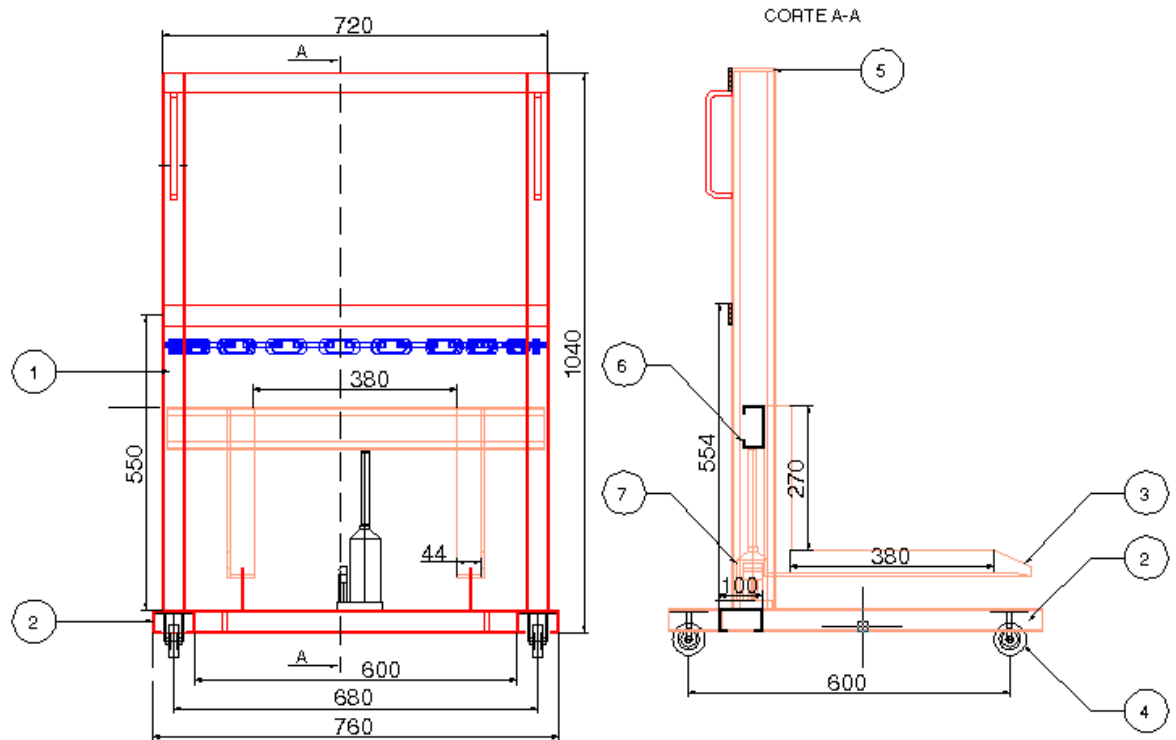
b. Elementos, partes y dimensiones del montacargas.
